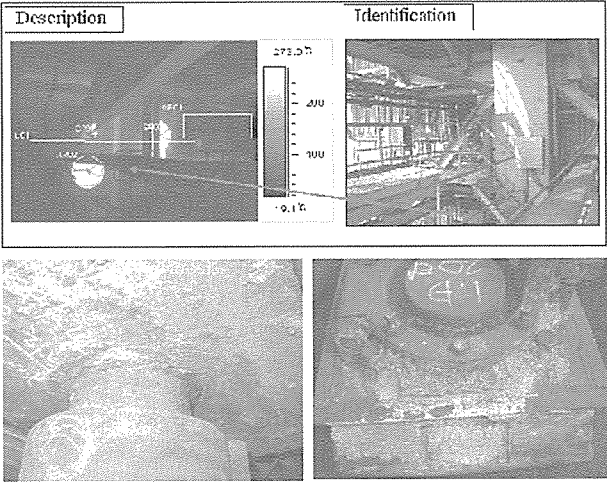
Expansion Joint Crack      [그림 2] HDR Casing Crack
